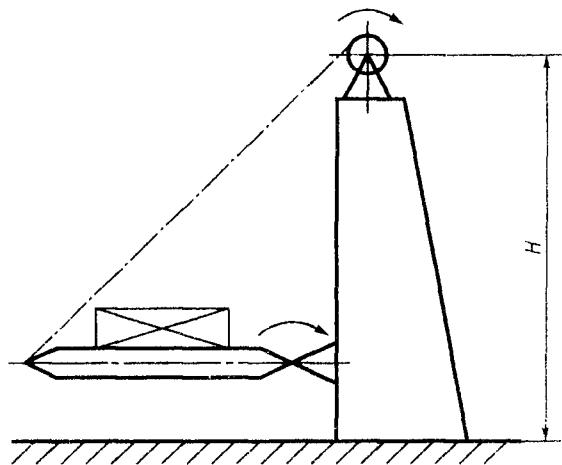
Кантователь рычажный с поворотной рамой
